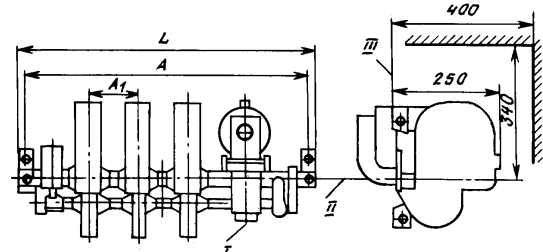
Габаритные и установочные размеры контакторов КТП6052 и КТП6053. Остальное - см. рис. 1
